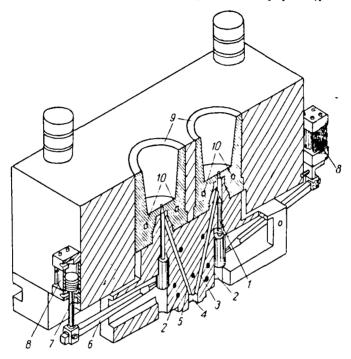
Прессформа с клапанными впусками и обогреваемыми литниковыми каналами:
